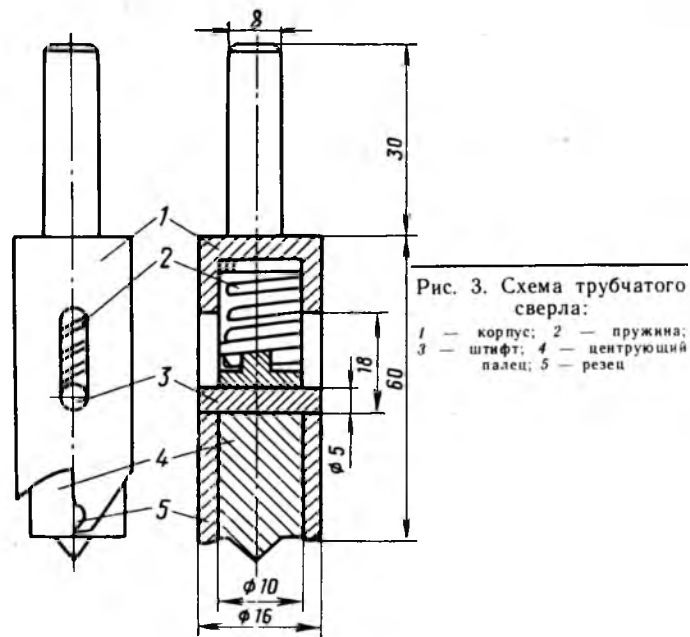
Схема трубчатого сверла: 1 — корпус; 2 — пружина; 3 — штифт; 4 — центрирующий палец; 5 — резец
